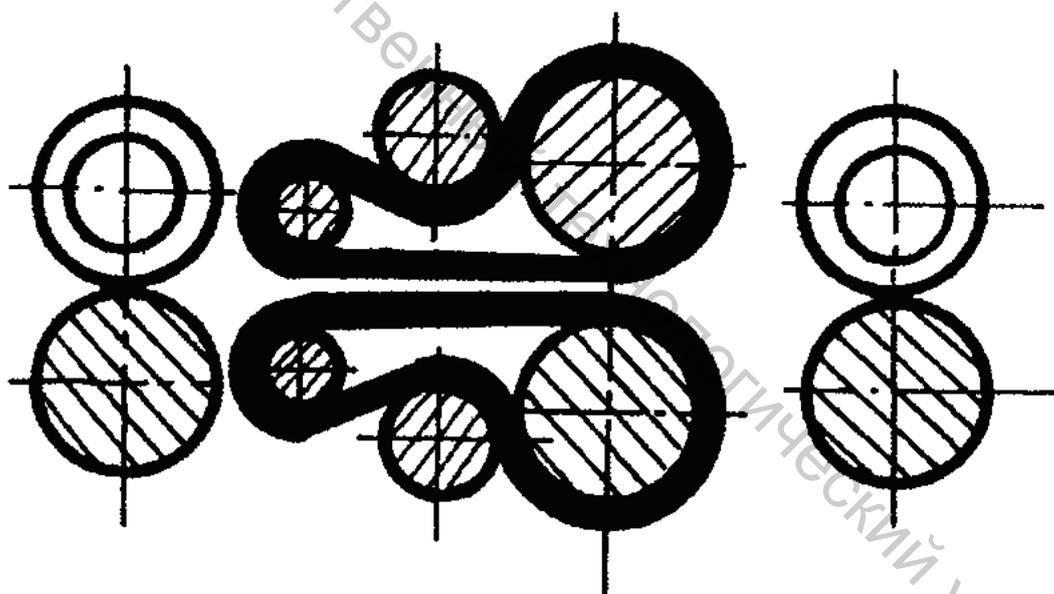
Схема двухремешкового вытяжного прибора конструкции Ф. Казабланки
